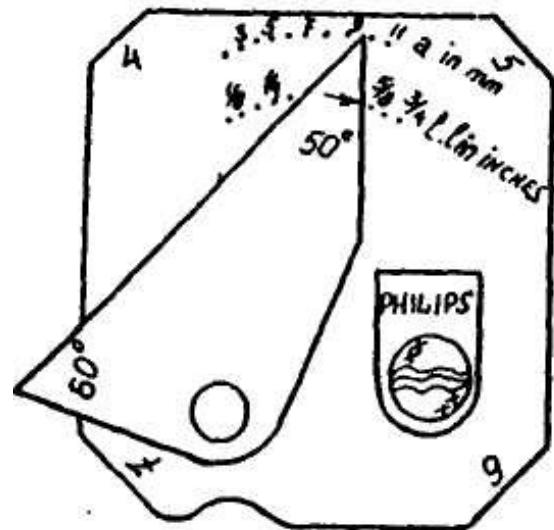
Шаблон для контроля сварных швов (фирма «PHILIPS»)
